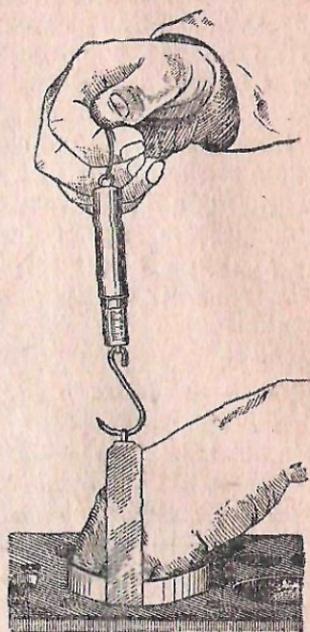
Проверка зазора между юбкой поршня и цилиндром
